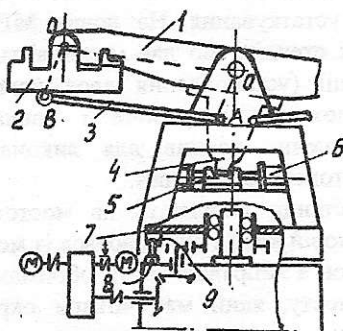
Схема поворотного розливного стенда: 1-несуча рама; 2-підвіски; 3-тяги; 4-зуб евольвентного профілю; 5-повзун; 6-плунжерні гідроциліндри; 7-поворотна платформа; 8-кругова рейка; 9-ролики
